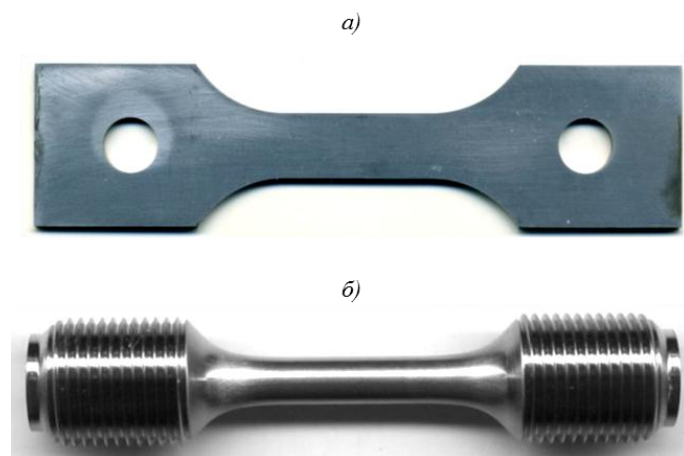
Общий вид образцов для проведения испытаний по схемам 1–3 (а) и 4–6 (б)
